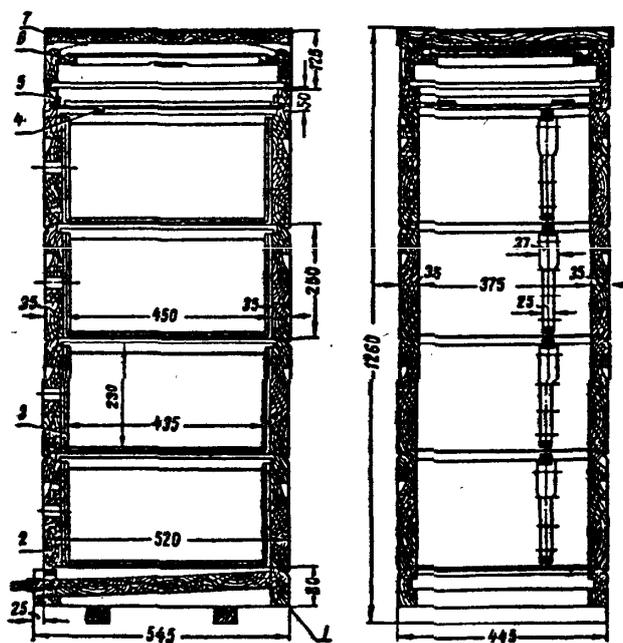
Схема устройства многокорпусного улья: слева — разрез вдоль рамок; 1 — дно; 2 — корпус; 3 — рамка; 4 — потолок; 5 — подкрышник; 6 — вентиляционная рама; 7 — крыша; справа — разрез поперек рамок.
